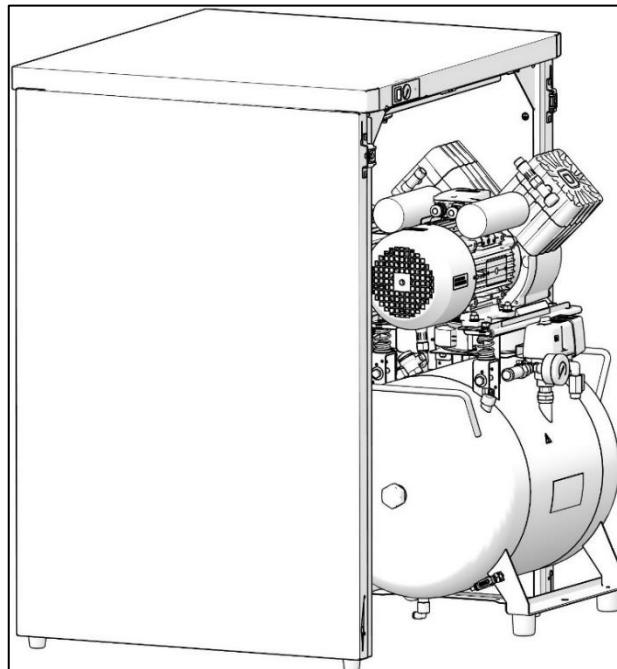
Positionierung des Kompressors für elektrische Anschlüsse
